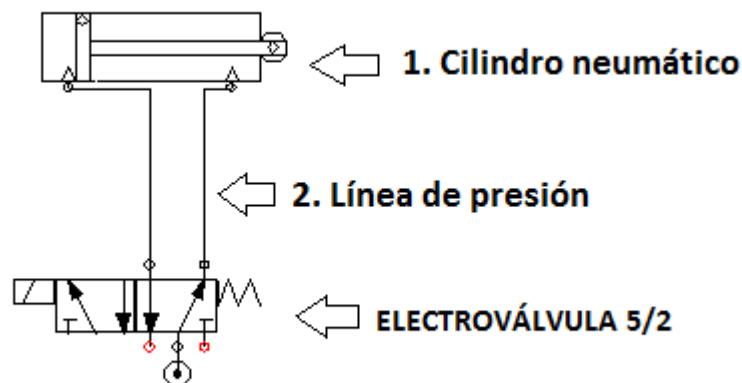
Esquema neumático de pinza de soldadura por puntos
